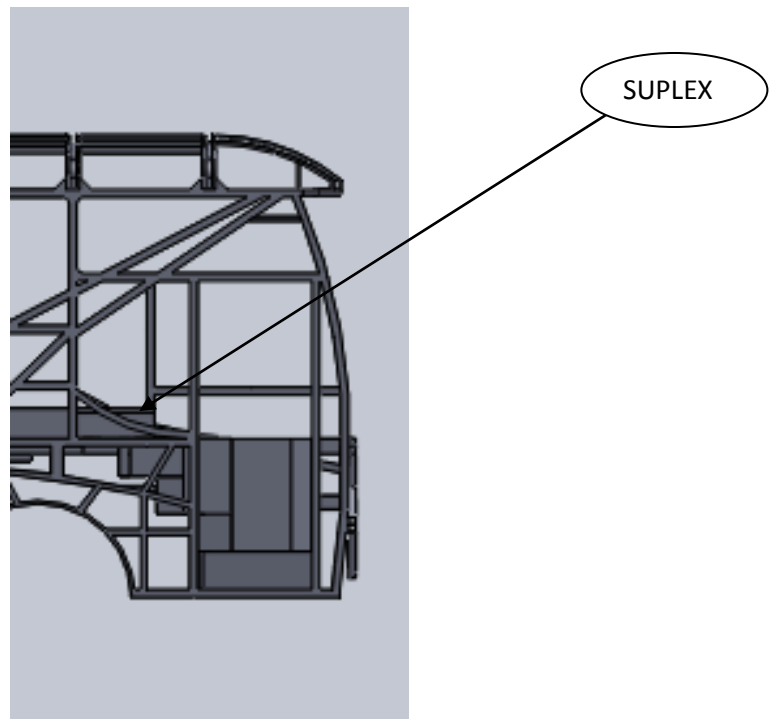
Detalle del Suplex en Vista Lateral de la Estructura Metálica de una Carrocería
